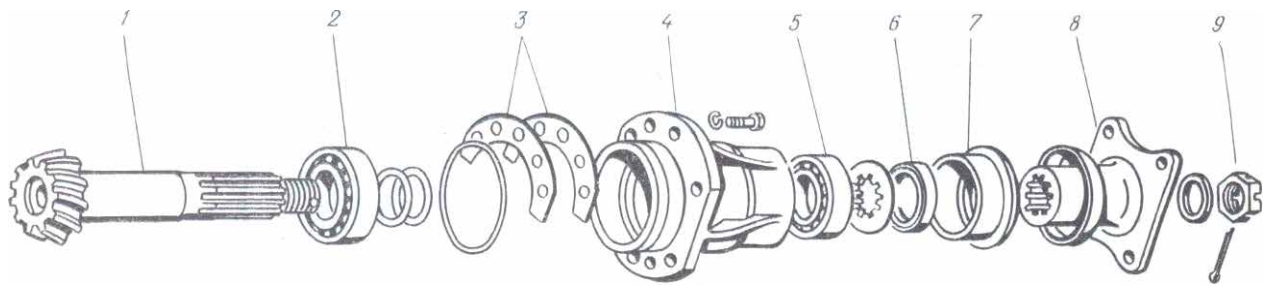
Взаємне розташування деталей головної передачі ведучого моста: 1 - провідна шестерня; 2,5 - підшипники; 3 - регулювальні прокладки; 4 - стакан; 6 - манжета; 7 - обойма сальника; 8 - фланець; 9 – гайка
